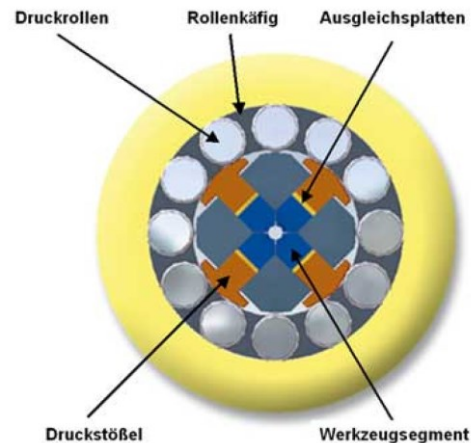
Prinzipieller Aufbau einer Rundknetmaschine.⁴⁹
